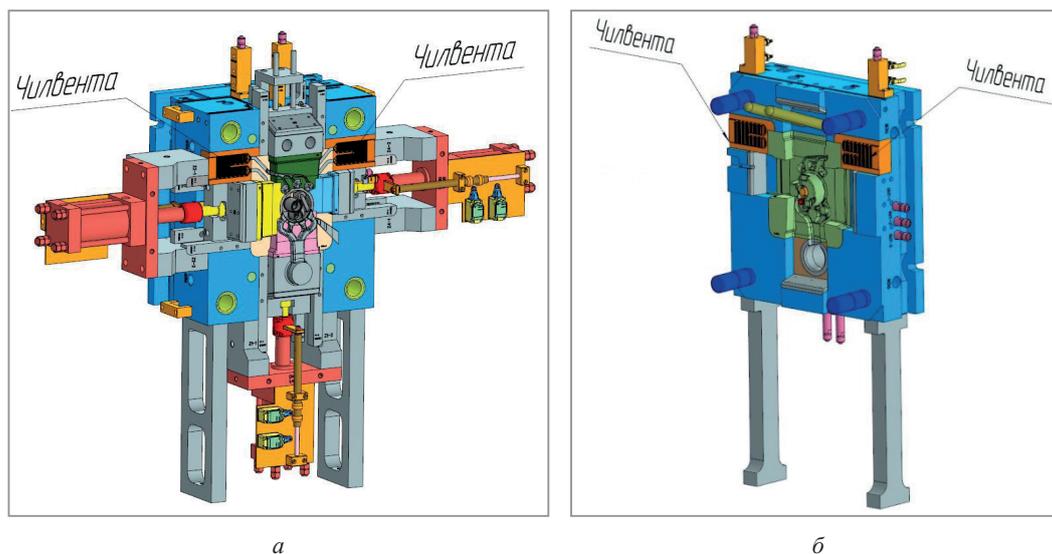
Пресс-форма с применением в конструкции двух чилвент:
